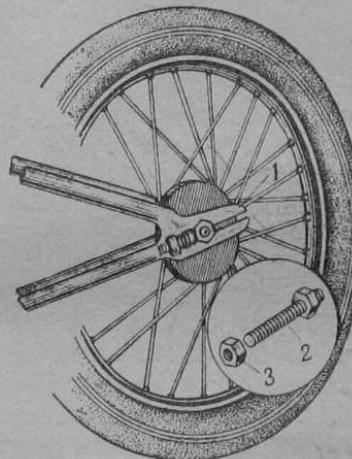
Натяжное устройство для цепи главной передачи М1А, К-125 и ИЖ-350:
